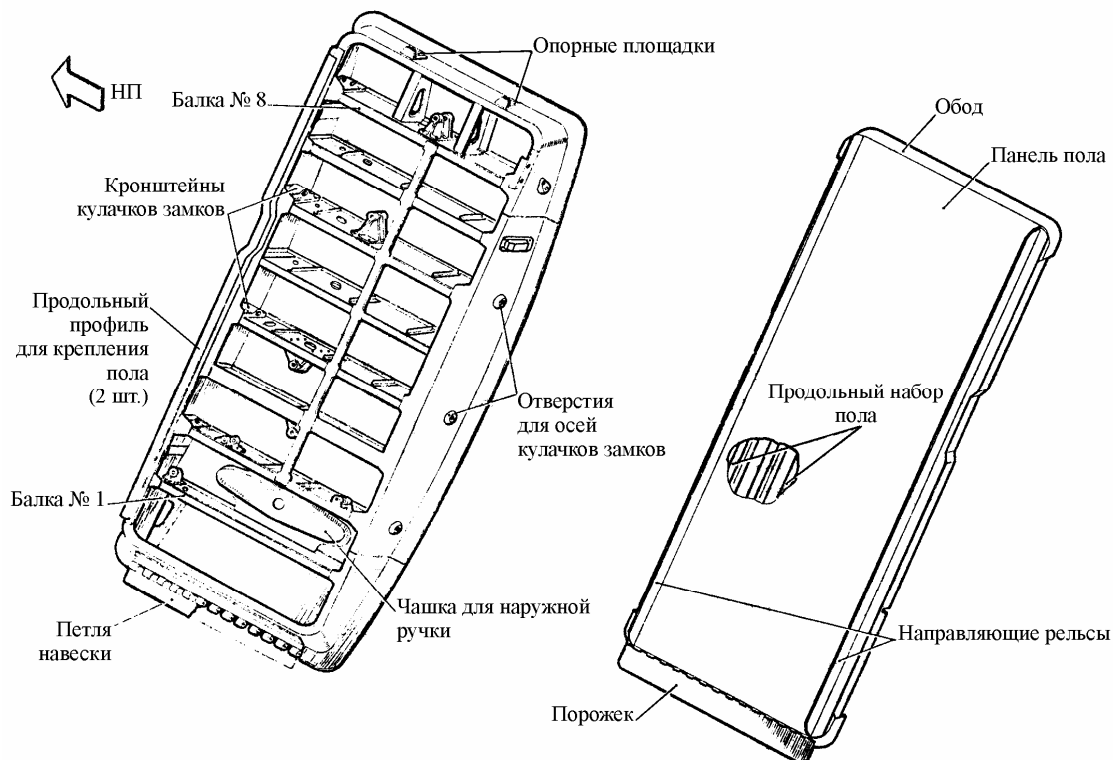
Крышка двери кухни (вид изнутри фюзеляжа)
